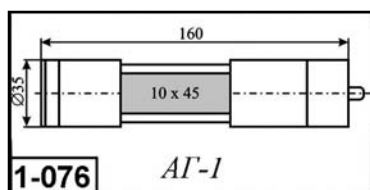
Внешний вид и габаритные размеры рентгеновского излучения
